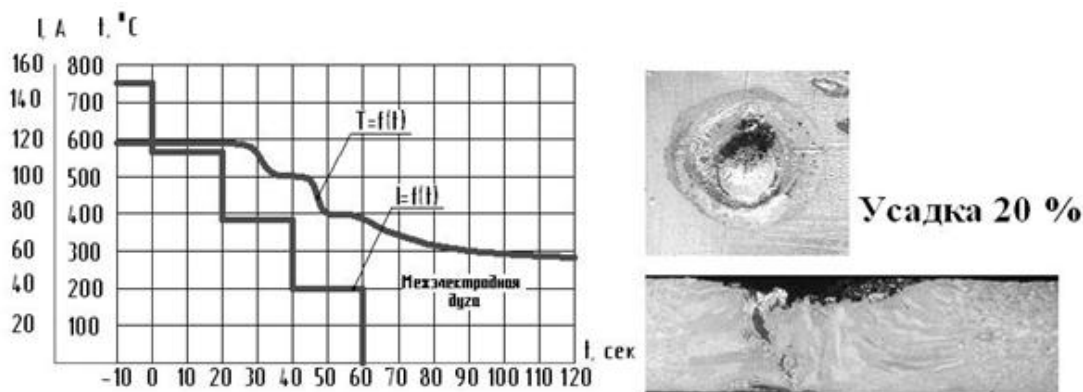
Термический цикл, форма и размеры усадочного кратера при реализации ступенчатой формы кривой спада тока сварки
